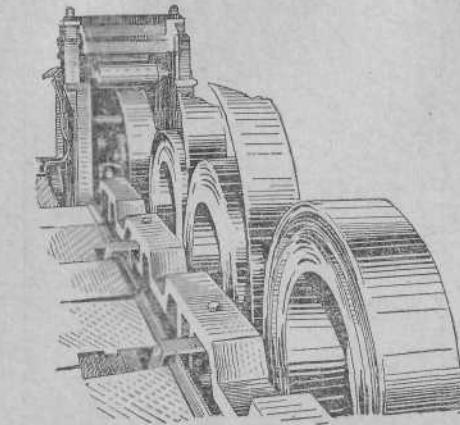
Загрузочные устройства профилегибочного агрегата 2-7×80-500.
